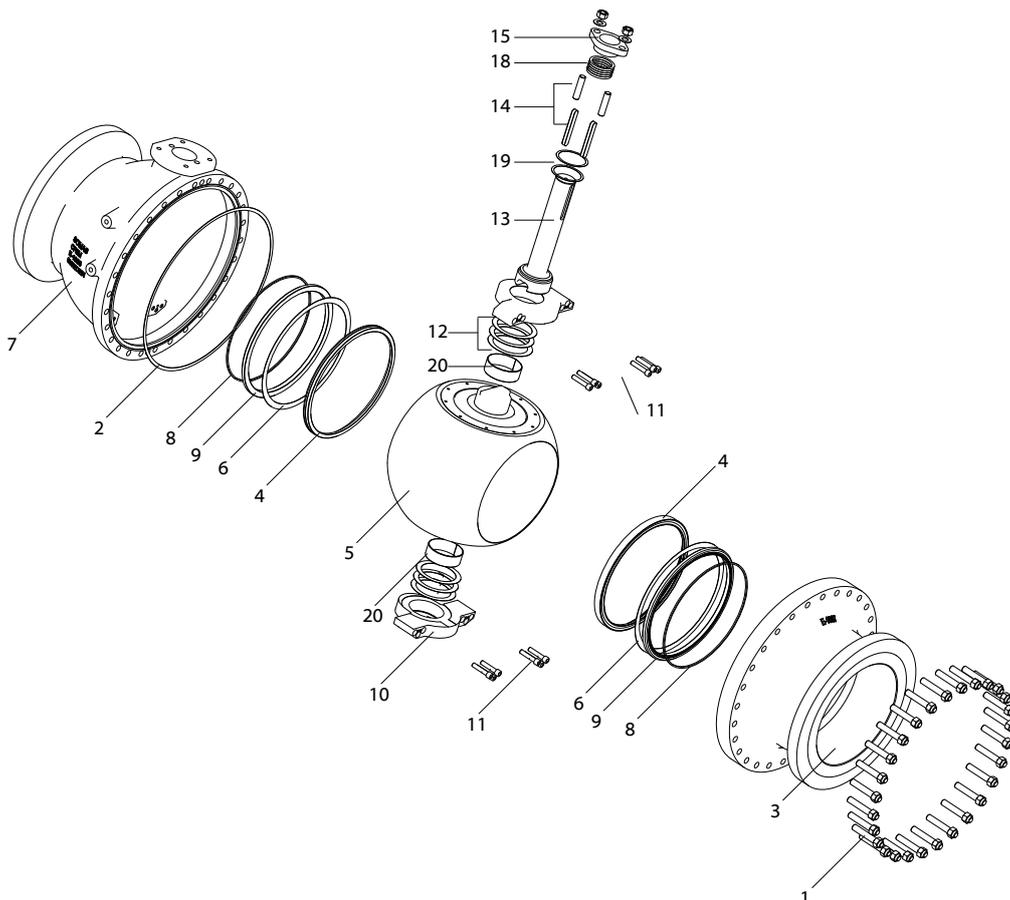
Substituição de assentos e esfera, DN 80-400
